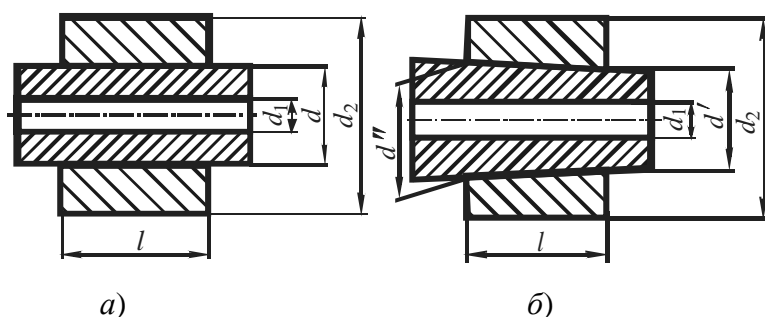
Схема соединения с натягом с цилиндрической (а) и конической (б) сопрягаемыми поверхностями
